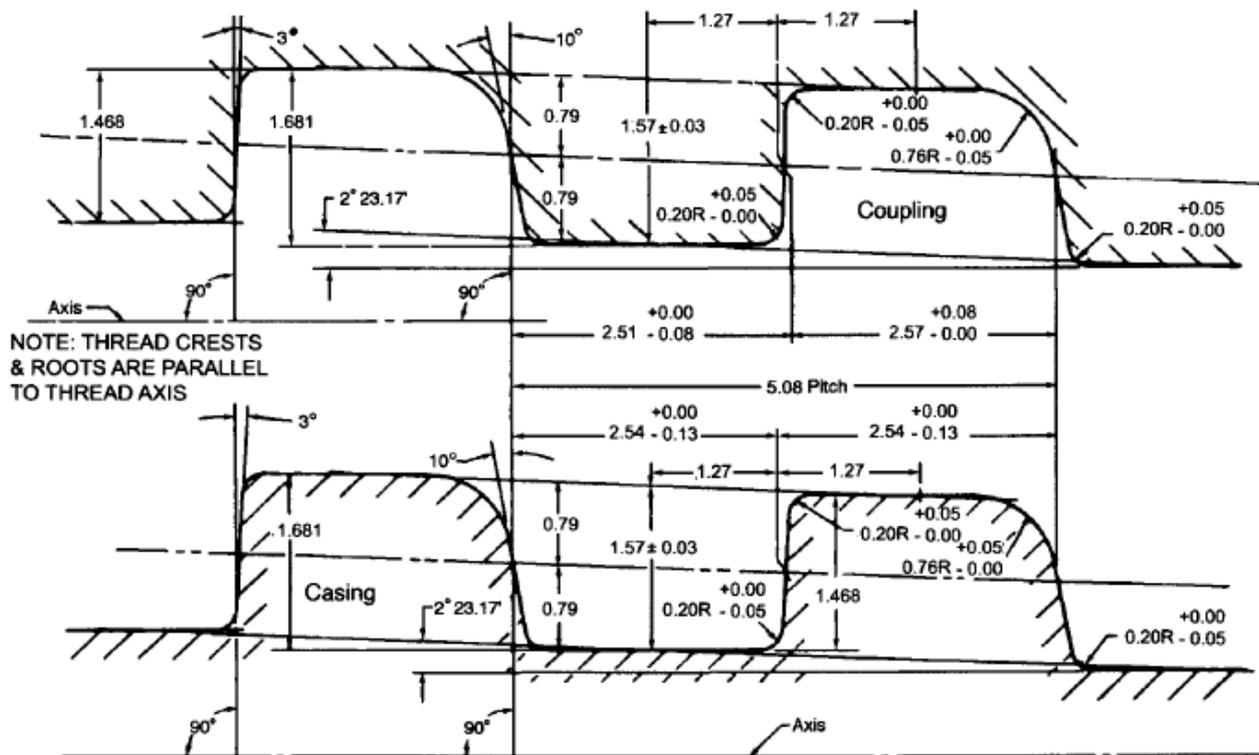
М. Основные размеры резьбы батресс для обсадных труб при ручном свинчивании
